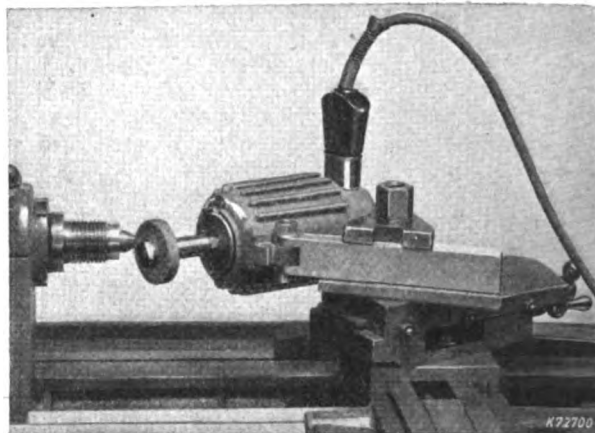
Universal-Spitzenschleifer beim Schleifen einer Drehbankspitze.
